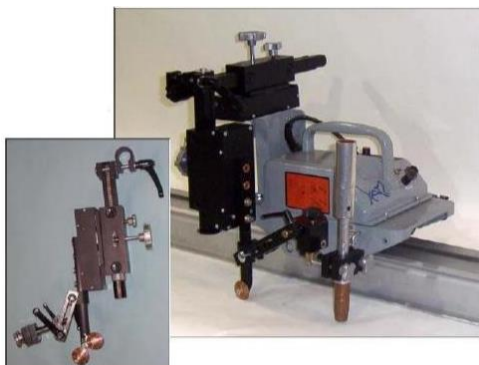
Sistema automatizado de soldagem com sensor de contato do tipo roda-mola [3].
